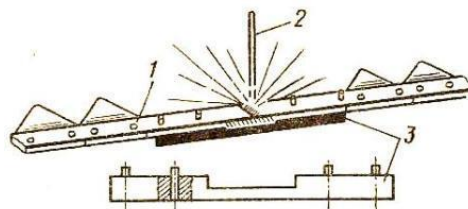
Сварка спинки ножа в кондукторе.
